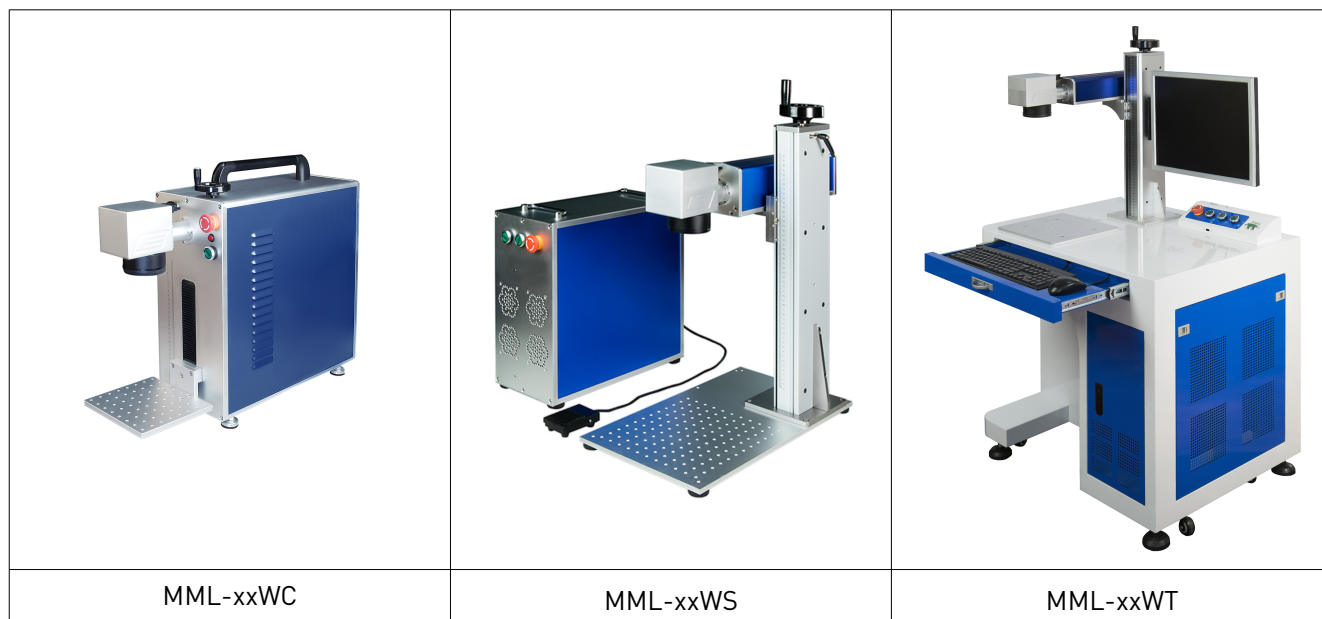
Внешний вид моделей лазерного маркировочного станка
